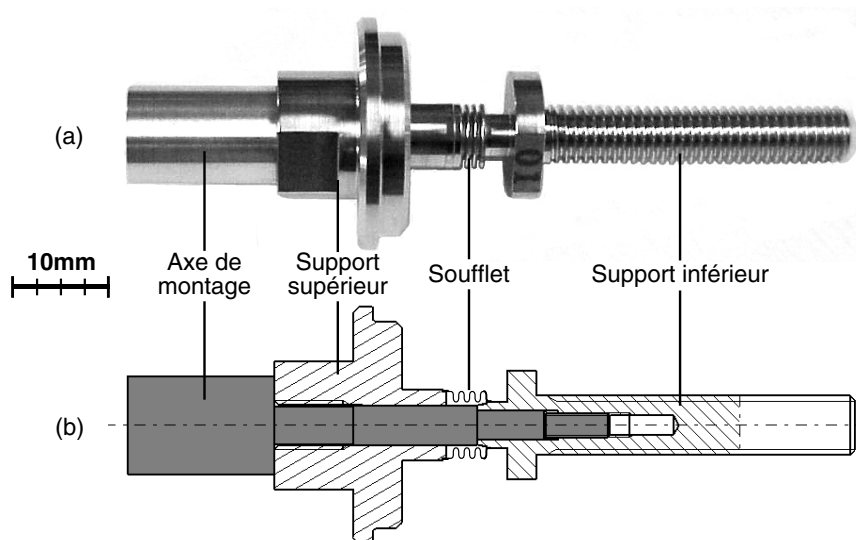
Détail du montage du soufflet dans le dispositif d'essais. a) Vue générale de l'éprouvette comportant le soufflet. Elle est équipée d'un axe de montage permettant d'assurer l'état initial libre du composant. b) Vue en coupe de l'ensemble.
